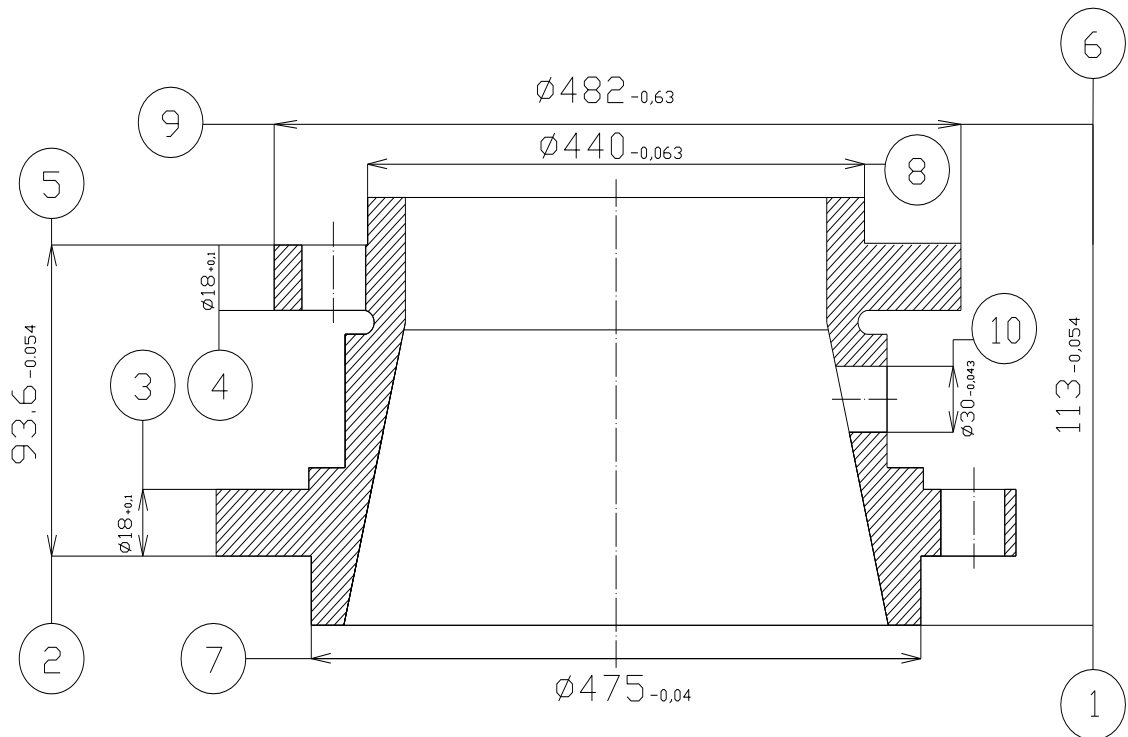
Ескіз деталі і нумерація оброблюваних поверхонь
